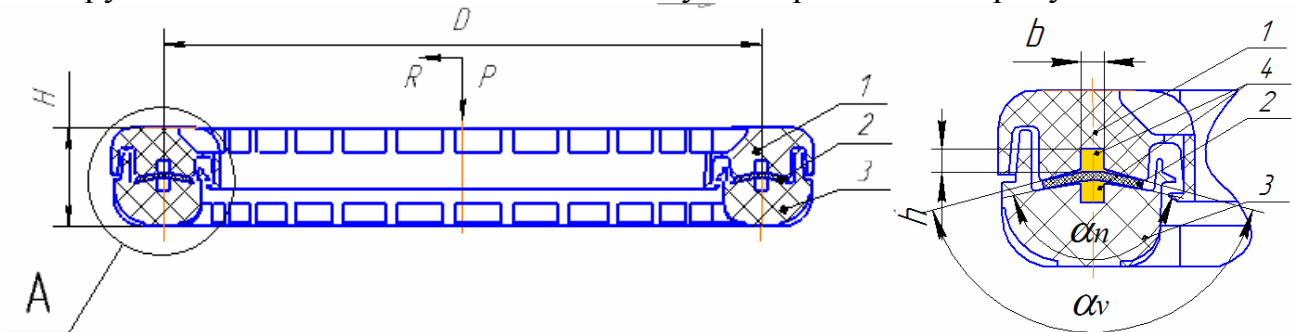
Конструкция опорного подшипника скольжения на масляной подушке: поперечное сечение подшипника (слева), поперечное сечение рабочей части подшипника (справа)
